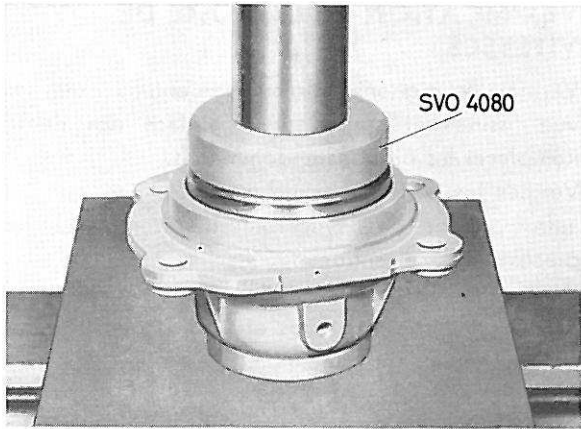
Montage du roulement à billes dans le couvercle arrière, nouveau modèle
